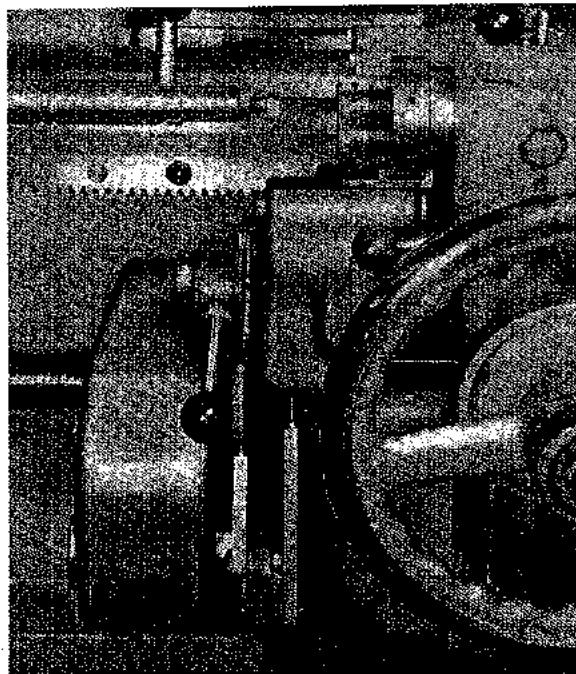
Accesorio para roscar con terraja (Jones & Lamson Machine Co.)
